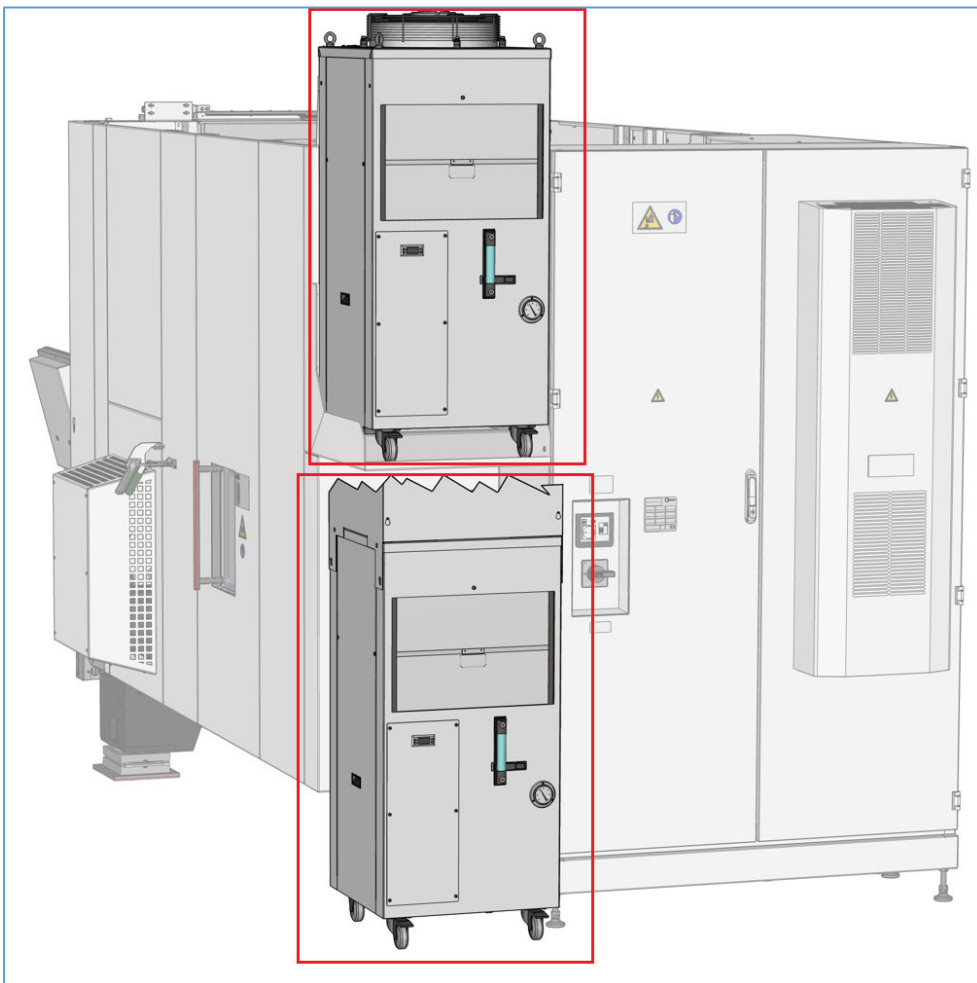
CNC-Werkzeugmaschine und einem Chiller (rot) für die Kühlung der WZM in Seitenmontage.
